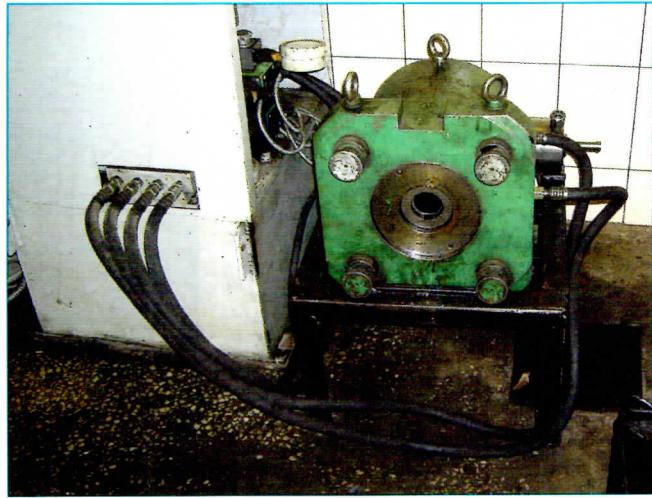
Гидросъемник для демонтажа-монтажа фланца полумуфты вала блока шестерен редуктора
